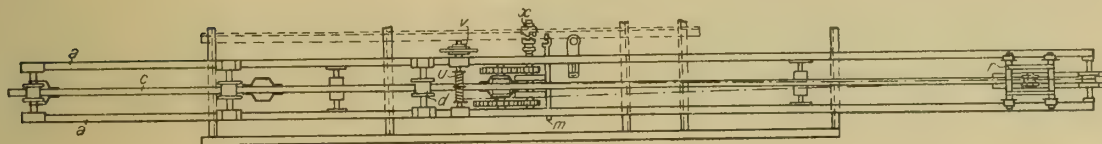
Grundriß der Planiervorrichtung von Heintzmann & Dreyer.
